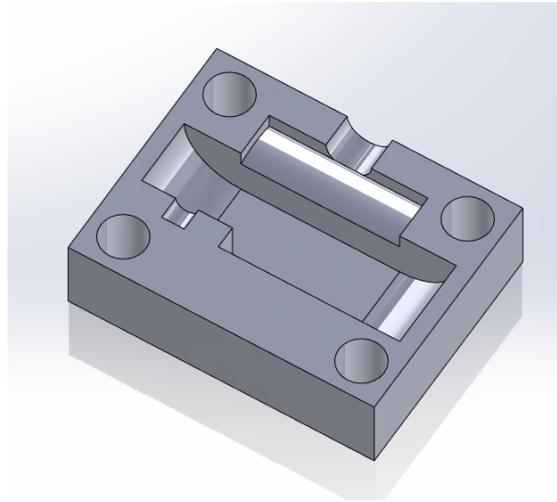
Molde de injeção da peça a colocar na zona de inserção de cabos no quadro
